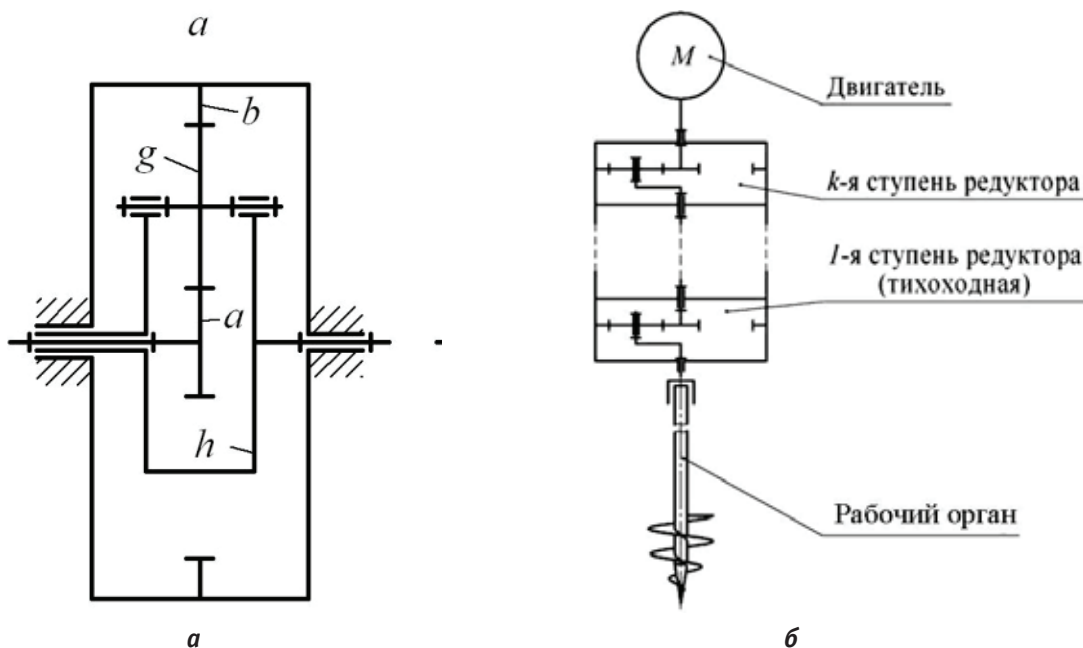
Схемы: *a* — планетарной передачи $2k-h$ с одновенцовыми сателлитами; *б* — привода
